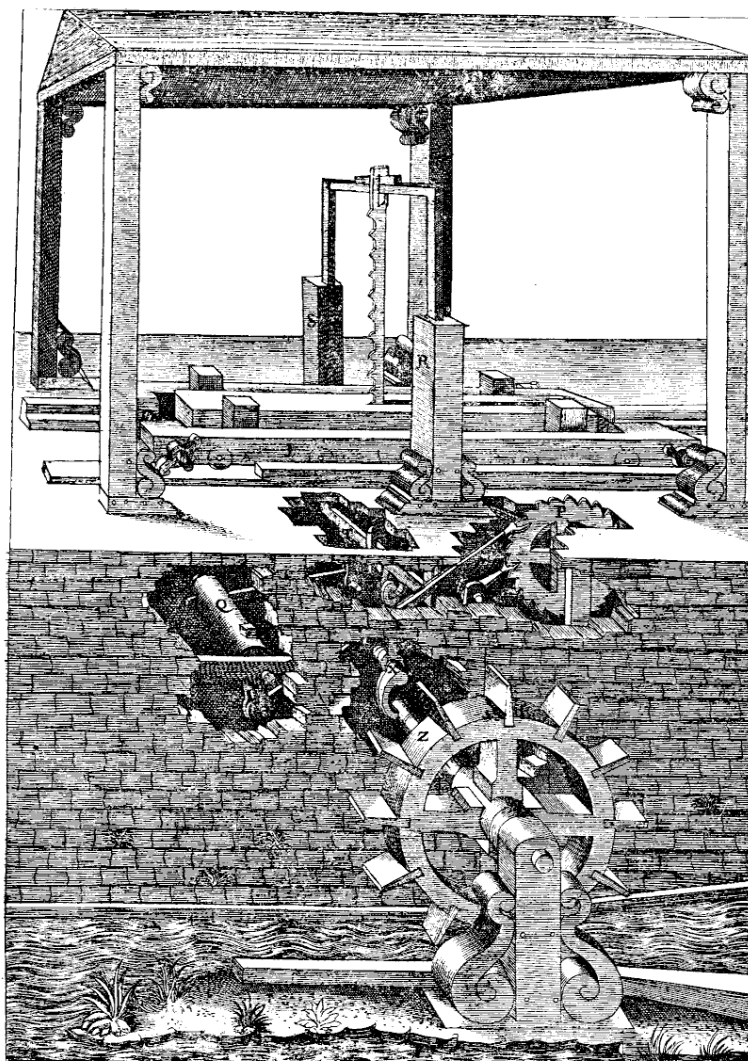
Machine à scier le bois au XVI^e siècle (RAMELLI).
